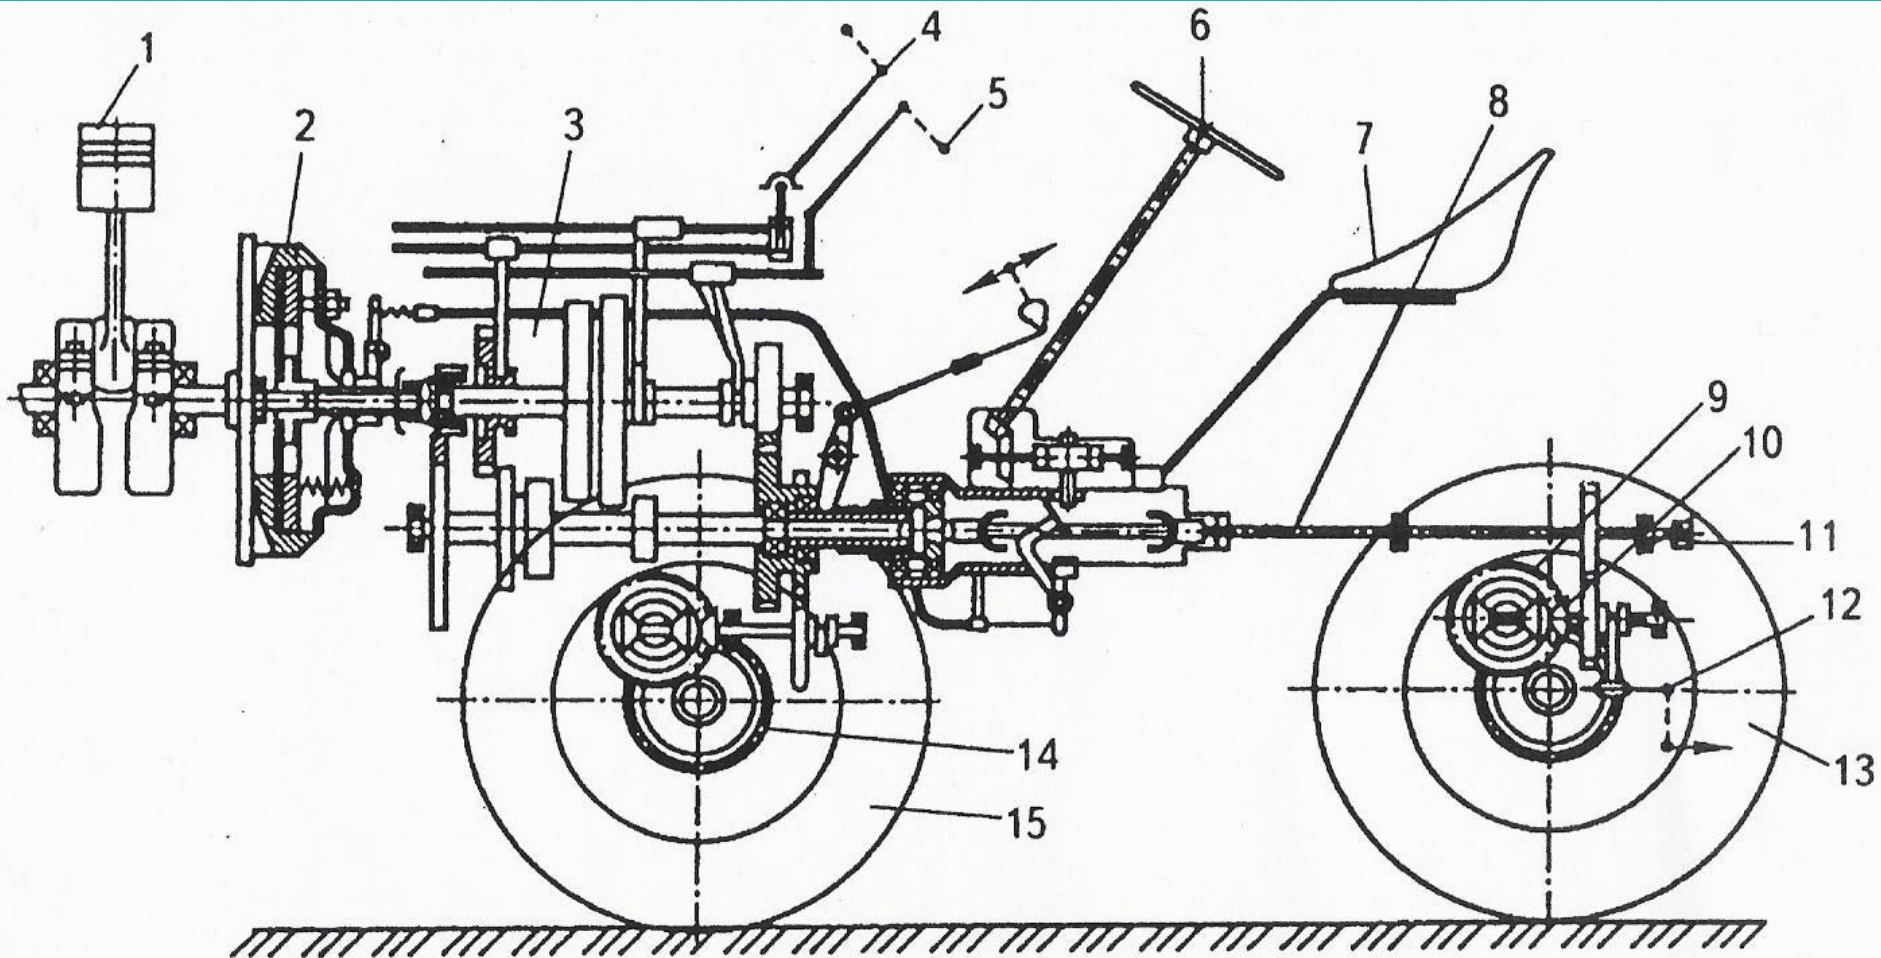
Общий вид малогабаритного трактора: 1 – двигатель; 2 – сцепление; 3 – коробка передач; 4 – рукоятка переключения передач; 5 – рычаг заднего хода; 6 – рулевое управление; 7 – сиденье; 8 – соединительный вал; 9 – главная передача заднего моста; 10 – дифференциал; 11 – вал отбора мощности; 12 – рычаг переключения; 13 – заднее колесо; 14 – конечная передача; 15 – переднее колесо
